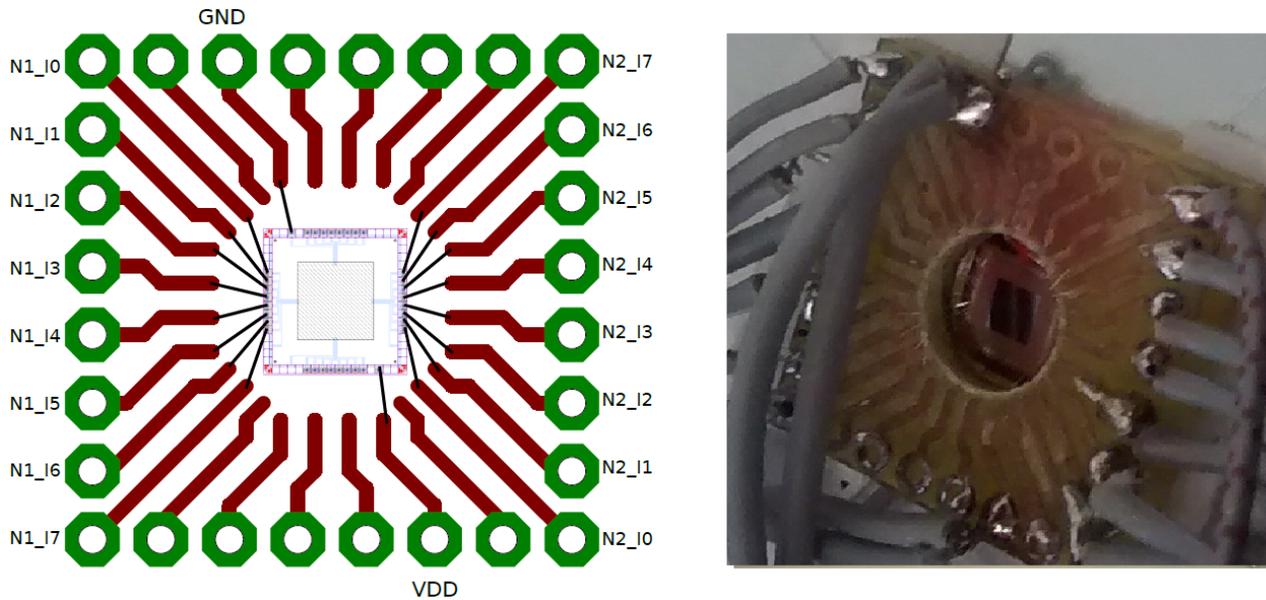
Diagrama de Solda (*wiremap*) do *Chip* sensor piezo-transdutor em PCB e foto do dispositivo encapsulado.
